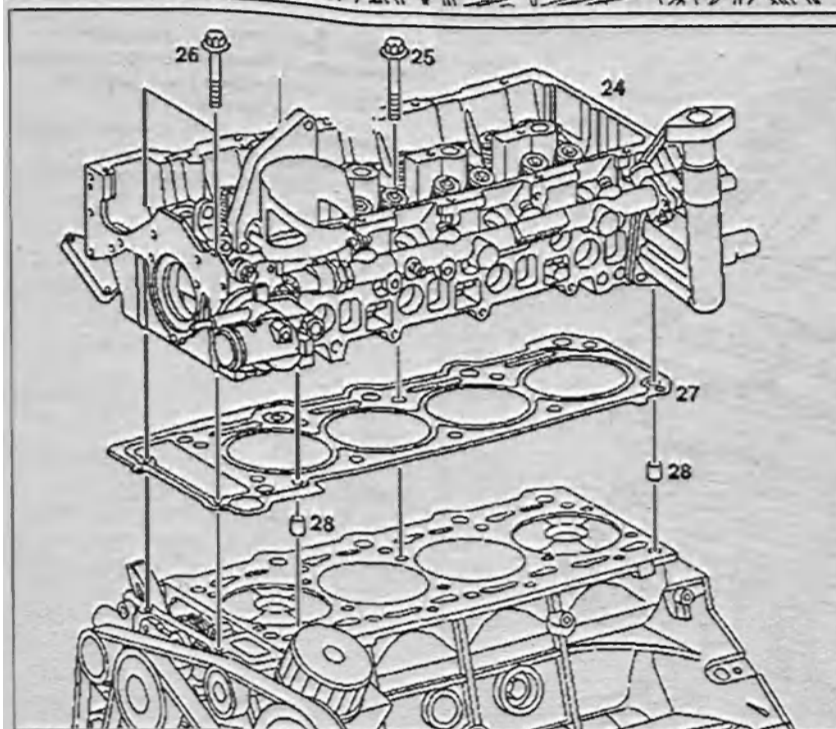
б. Снятие и установка головки блока цилиндров (показано на двигателях 611):
